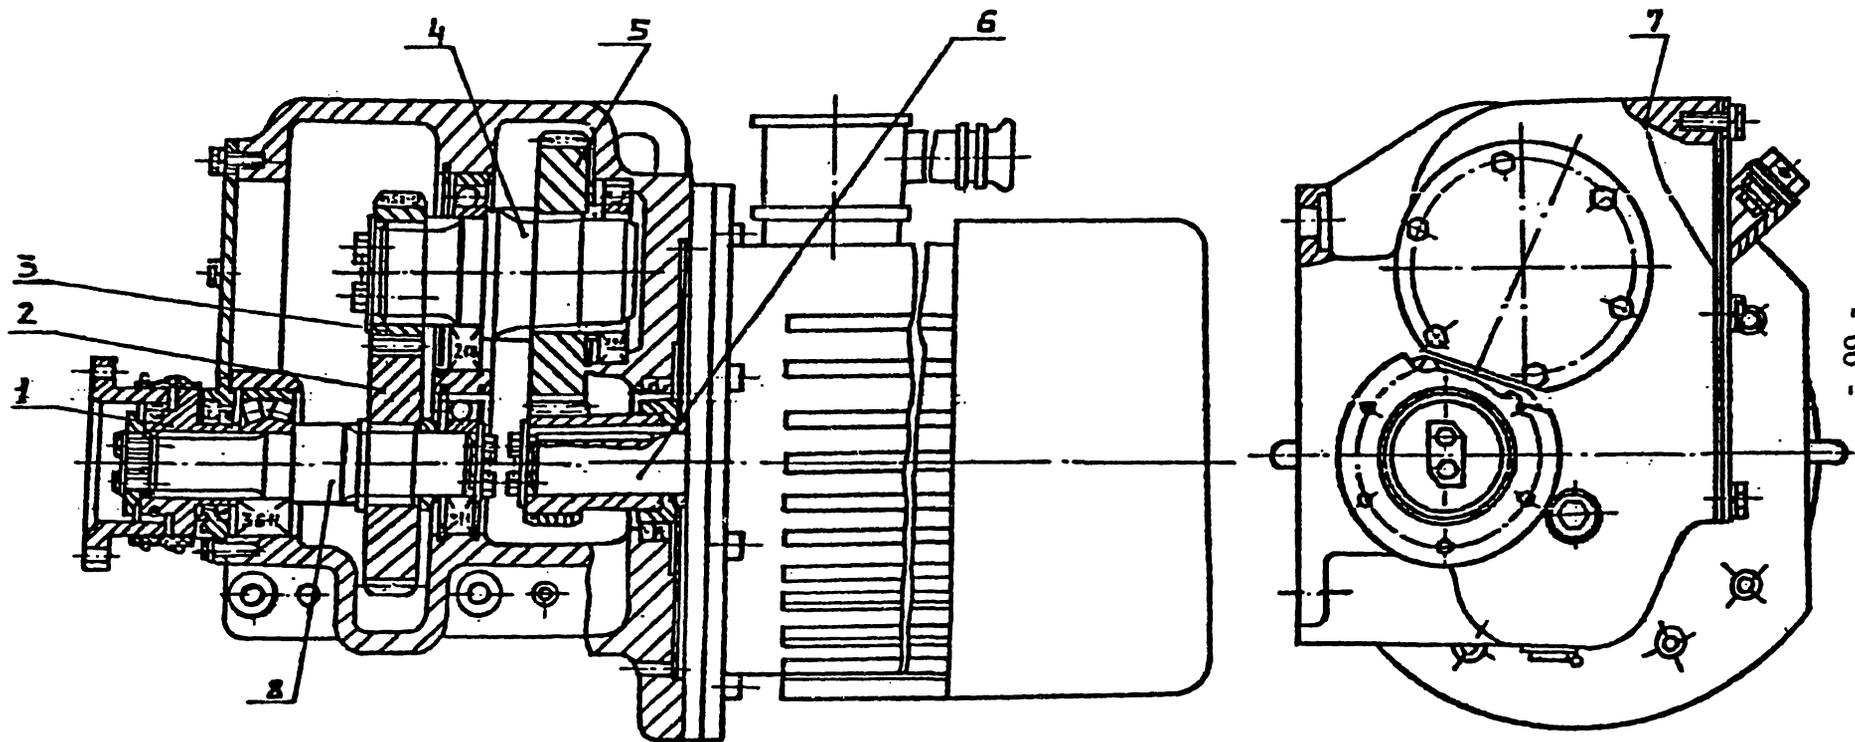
Редуктор цилиндрический конвейера «Урал-20Р» :
